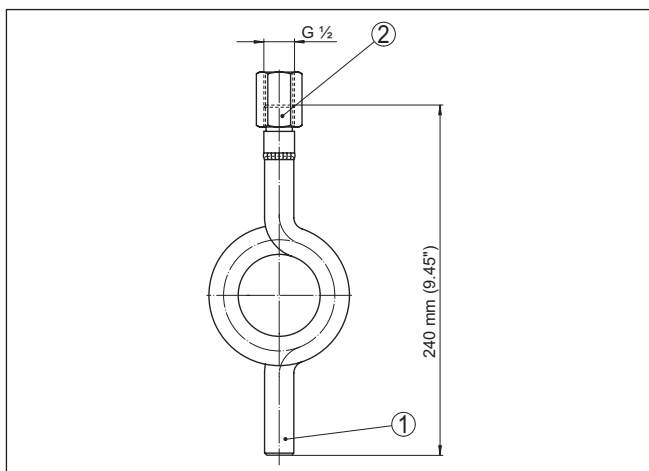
Сифон соотв. DIN 16282, кругообразный для вертикального отбора давления, форма D
